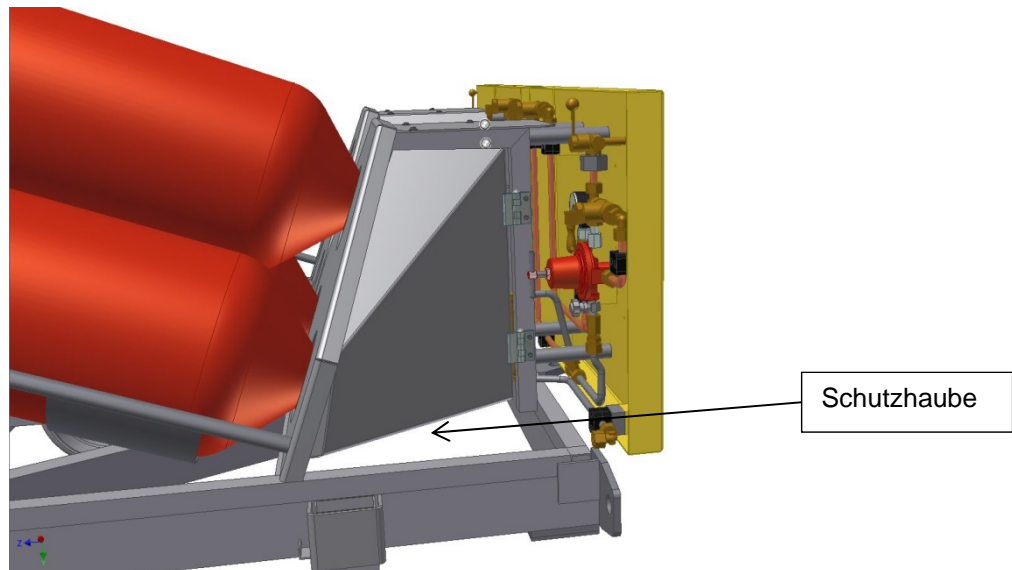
Ansicht SH12 –S mit geschlossener Schutzhaube (Prinzipdarstellung)
